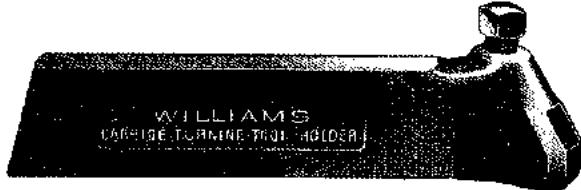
Soporte de herramienta acodado a izquierda (J. H. Williams & Co.)
